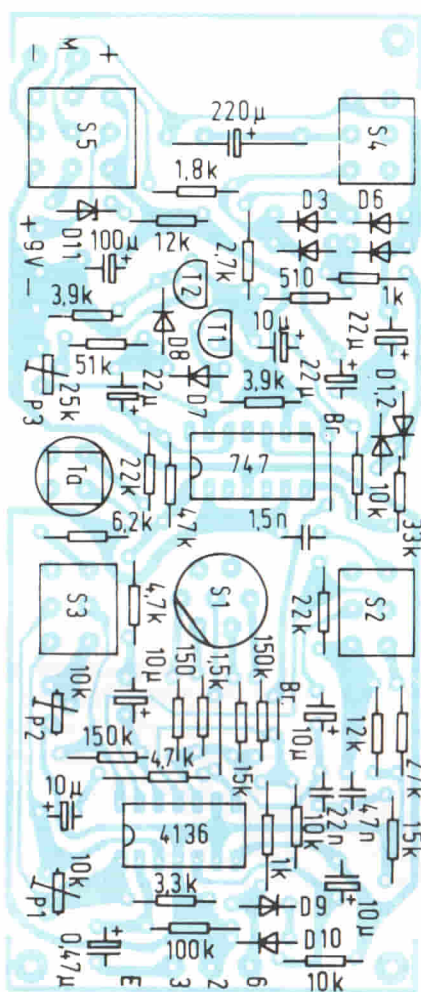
Disposizione dei componenti sul circuito stampato.
